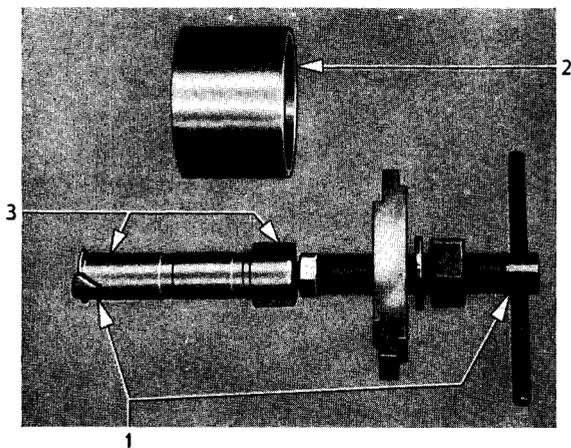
Spezial-Werkzeug zum Herausziehen der inneren Buchse aus Lenkgehäuse
